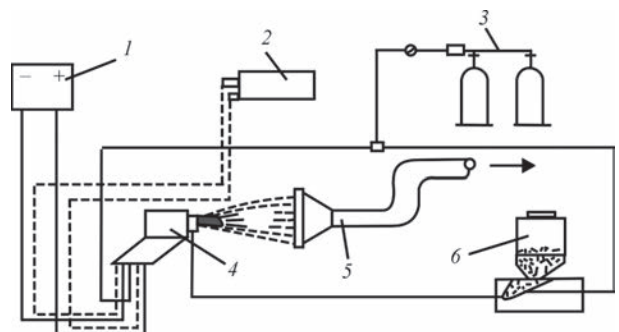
Схема установки плазмового напилення: 1 — джерело живлення; 2 — смінь з охолоджувальною водою; 3 — плазмотворюючий газ; 4 — плазмотрон; 5 — вентиляція; 6 — порошковий дозатор
